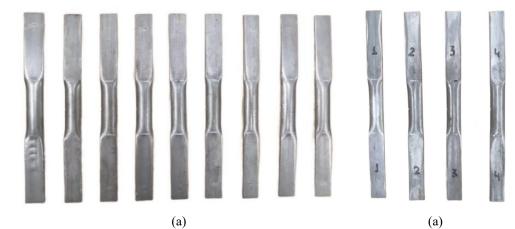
Фото образцов из стали 12X18H10T: (a) — изготовленных из новой трубы диаметром D = 25 мм; (б) — изготовленных из трубы диаметром D = 25 мм после эксплуатации (вторая часть испытаний)
